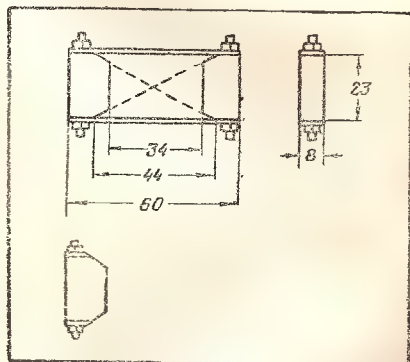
Разметка пакета и готовый башмак статора (снизу)
